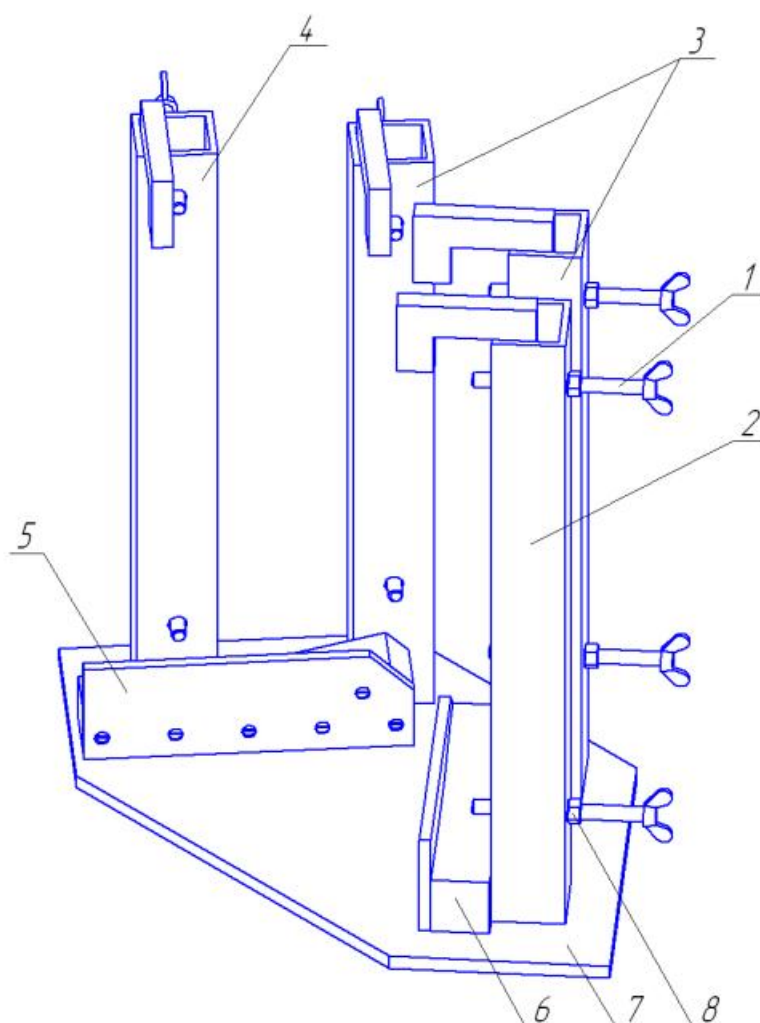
Приспособление для «сварки домика»
